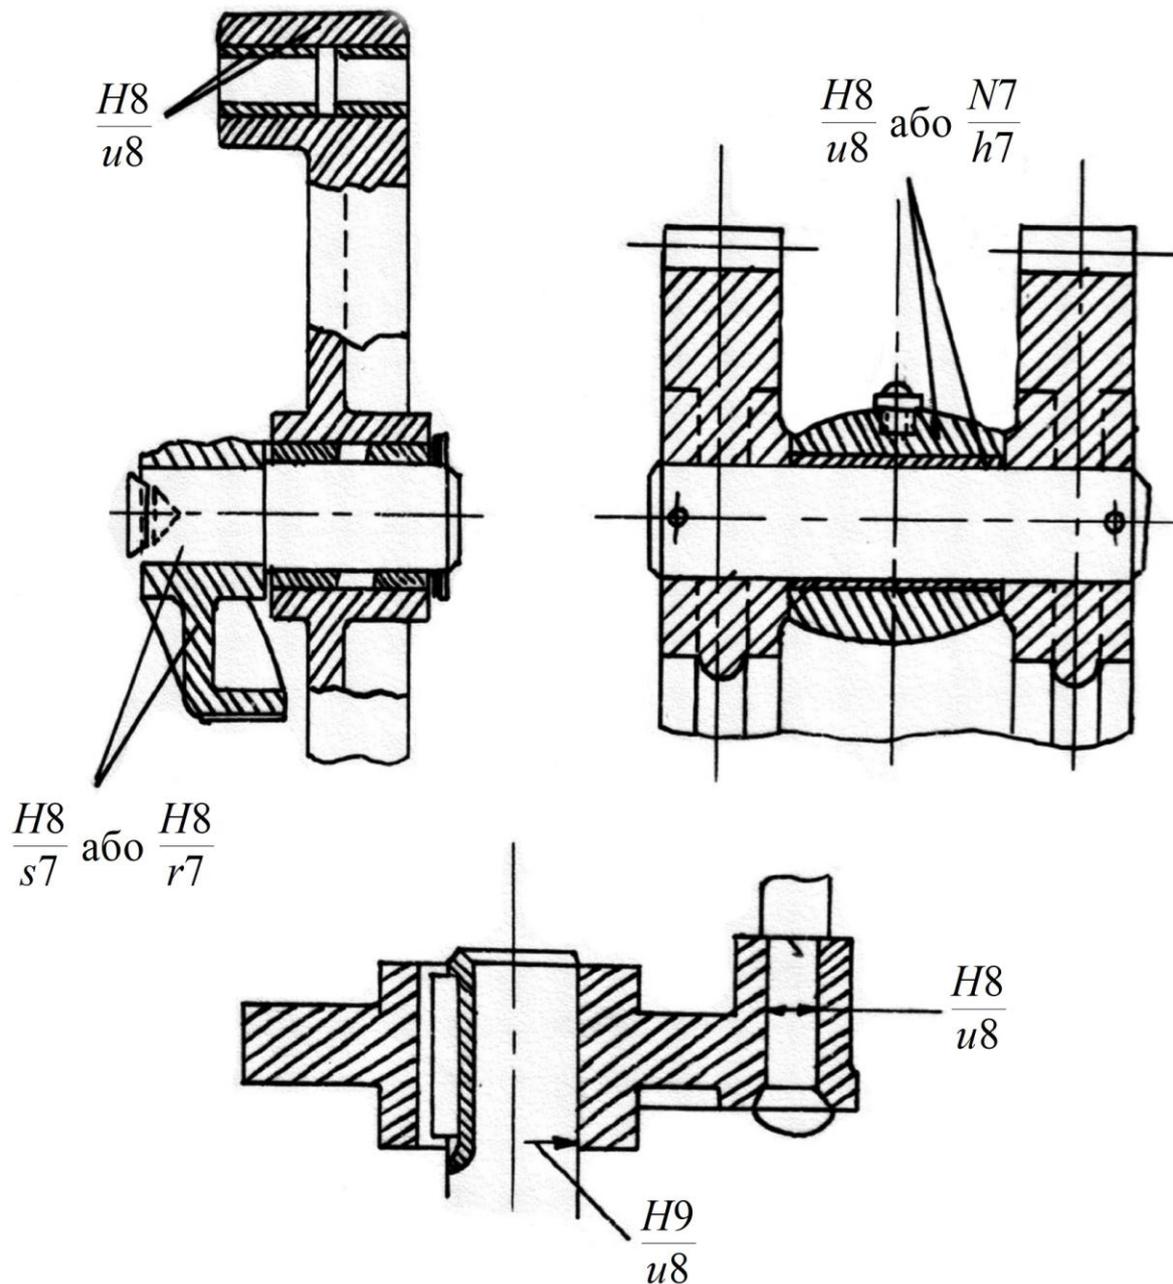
Приклади застосування посадок з натягом: а – важіль приводу зернозбирального комбайну; б – кривошипні шестерні сінного преса; в – кривошип косарки для косозубчастого циліндричного, прямозубчастого конічного і черв'ячного коліс
